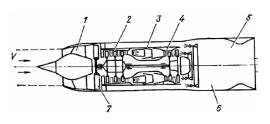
Схема ТРДДФ: I — входное устройство (воздухозаборник); 2 — компрессор; 3 — основная камера сгорания; 4 — газовая турбина; 5 — форсажная камера сгорания; 6 — выходное устройство (реактивное сопло); 7 — вентилятор
